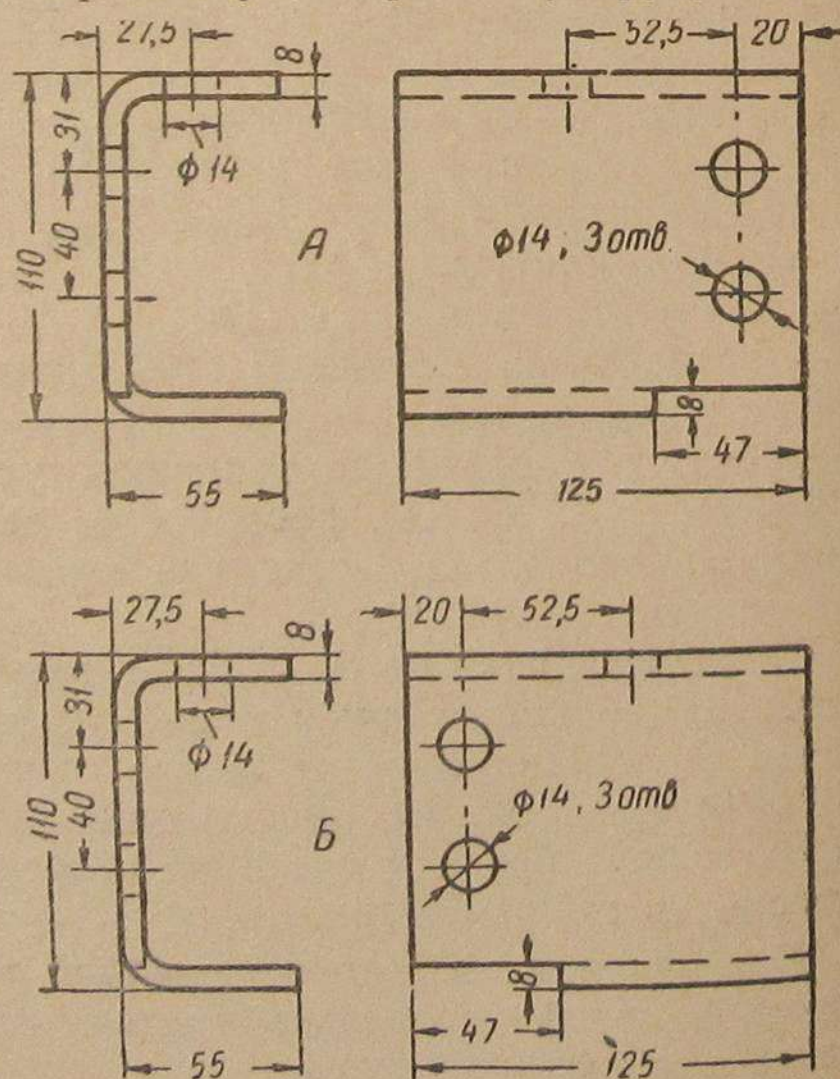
Подставки переднего бруса платформы: А — левая, Б — правая
